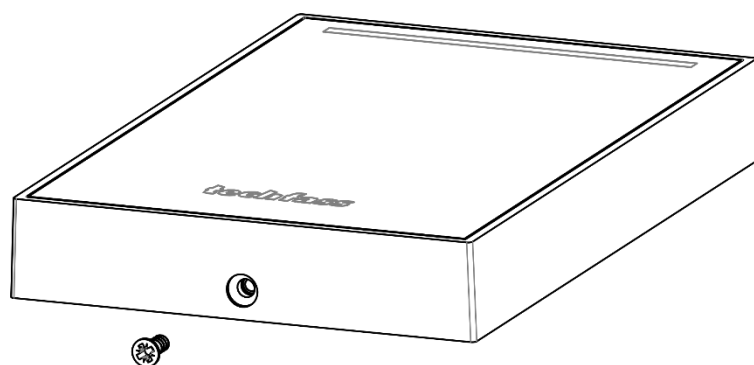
Assemblage des pièces à l'aide d'une vis de fixation
